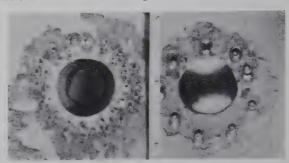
Kontaktfläche einer mit Bleimennige gestrichenen und mit gesiebtem Gußeisenschrot SS 14 (links) sowie Kügelchen B 1—8 (rechts) verbesserten Verbindung
